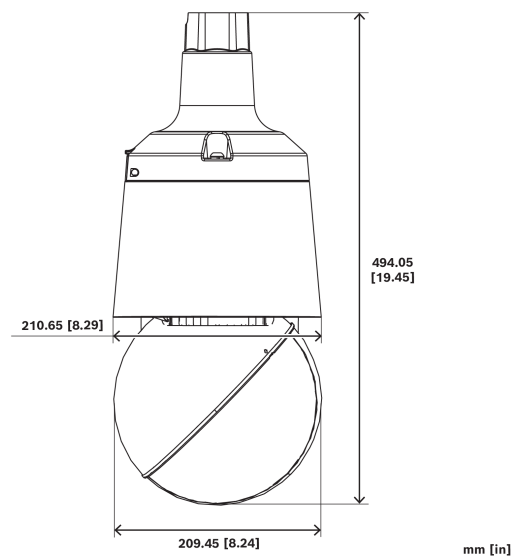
Dimensions en mm de la caméra installée sur NDA-7100-PIPE | NDA-7100-PIPEF (montage sur tube) Pour plus d'options, voir [Accessoires caméra - Guide de sélection rapide](#).
